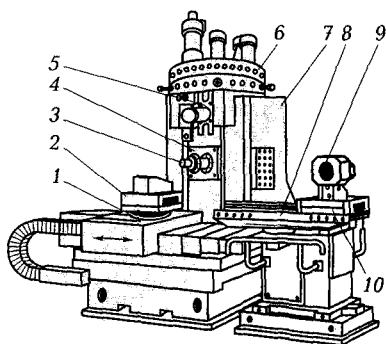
Многоцелевой станок с числовым программным управлением для обработки корпусных деталей: 1 — поворотный стол; 2 — зажимное приспособление; 3 — шпиндель; 4 — шпиндельная бабка; 5 — автооператор; 6 — инструментальный магазин; 7 — подвижная стойка; 8 — перегрузочное устройство; 9 — заготовка; 10 — паллета
